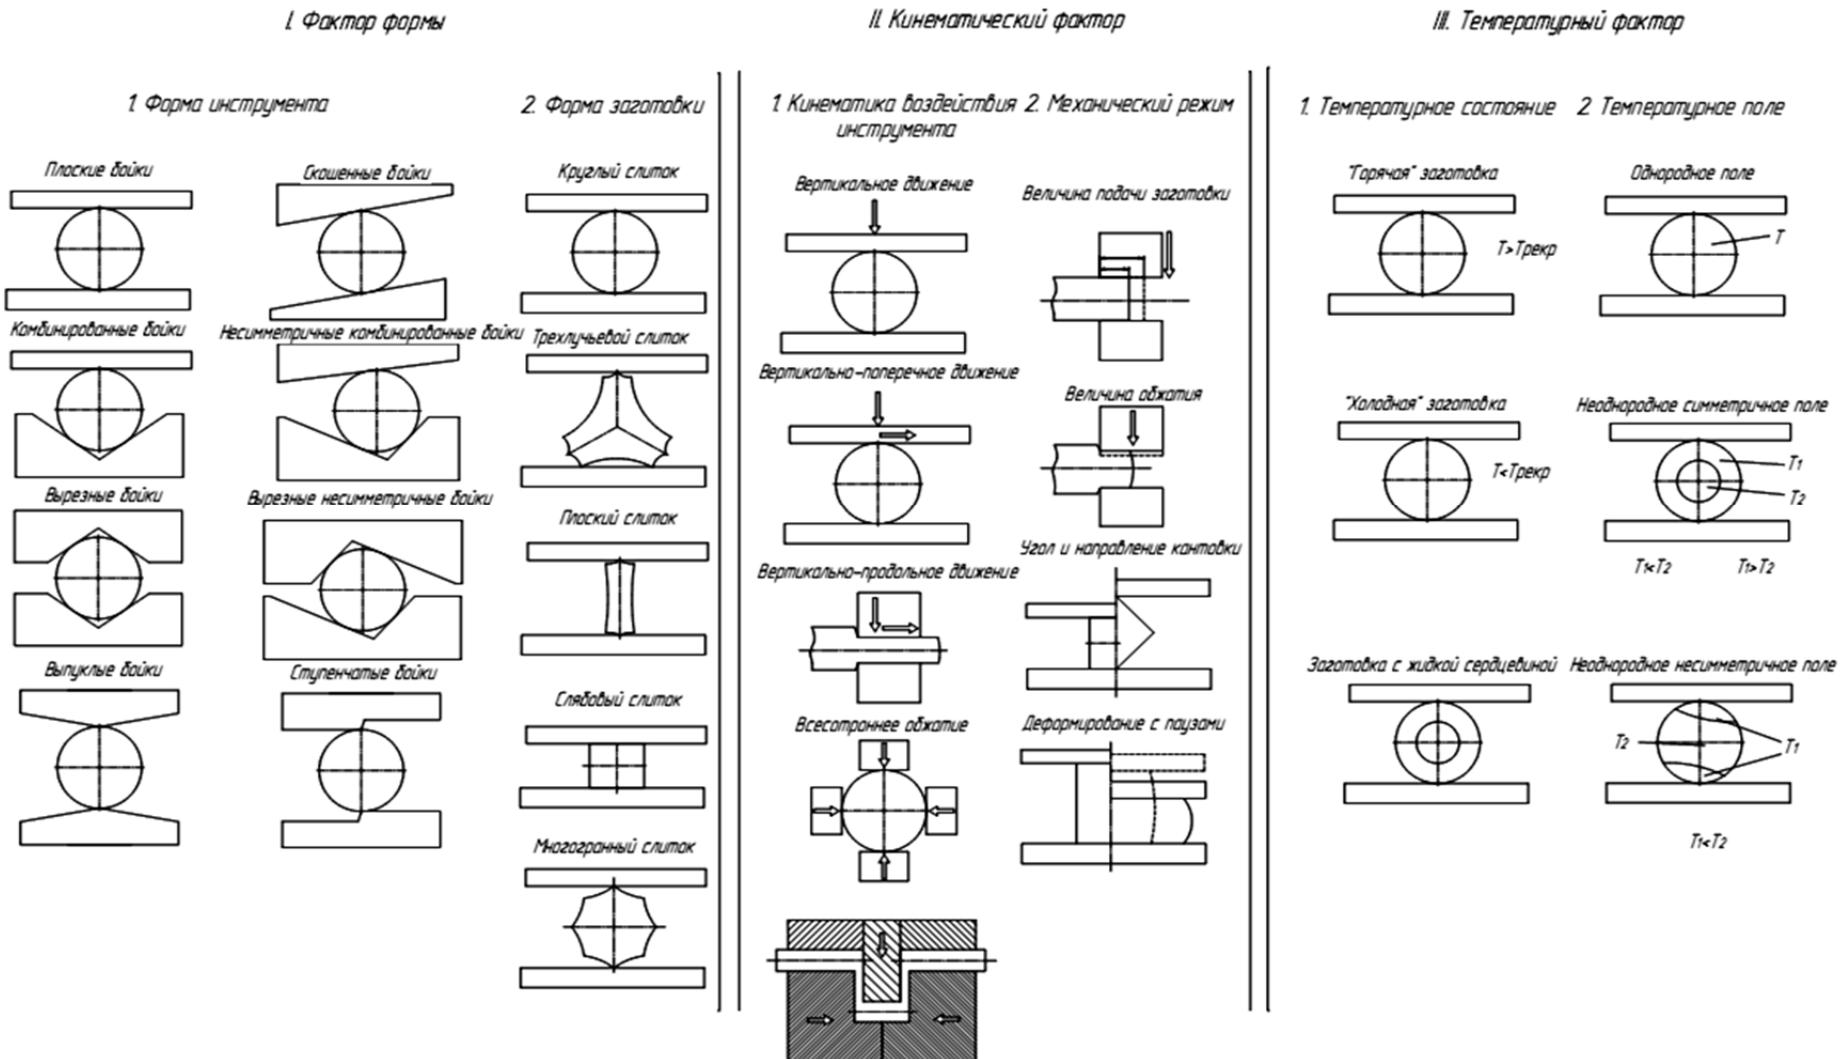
Приемы ковки, позволяющие управлять напряженно-деформированным состоянием заготовки
